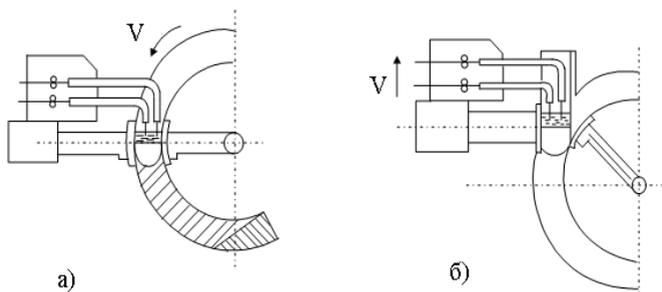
Схема процесса электрошлаковой сварки кольцевого стыка:
